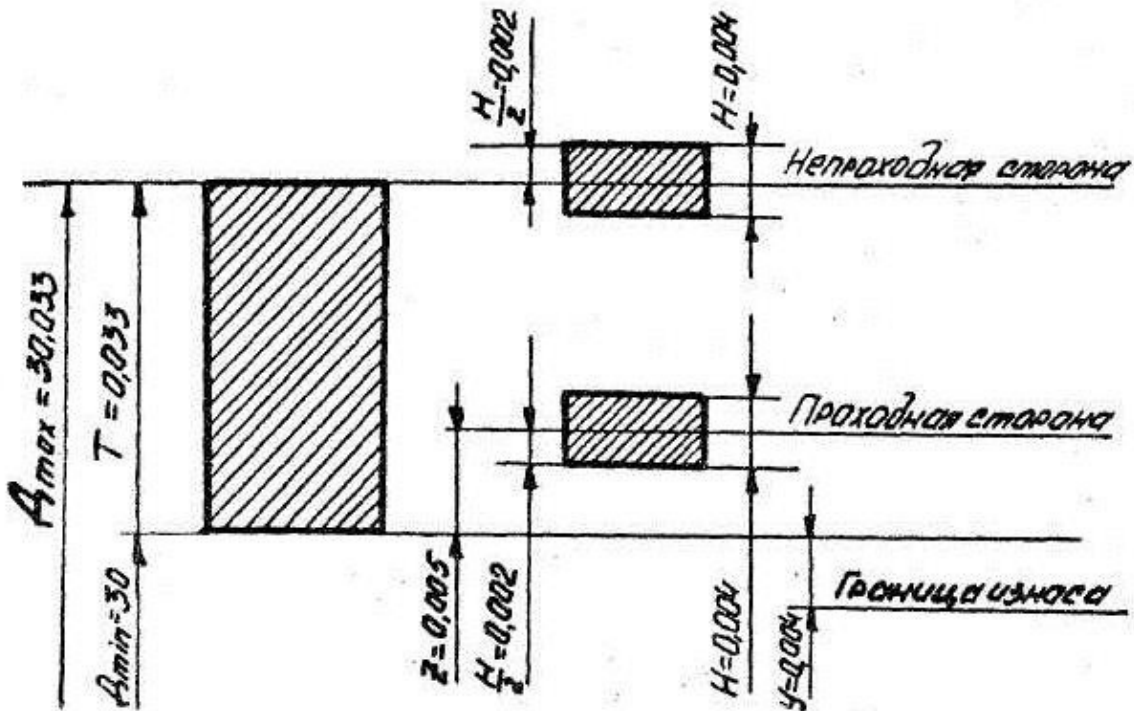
Схема расположения полей допусков калибров
